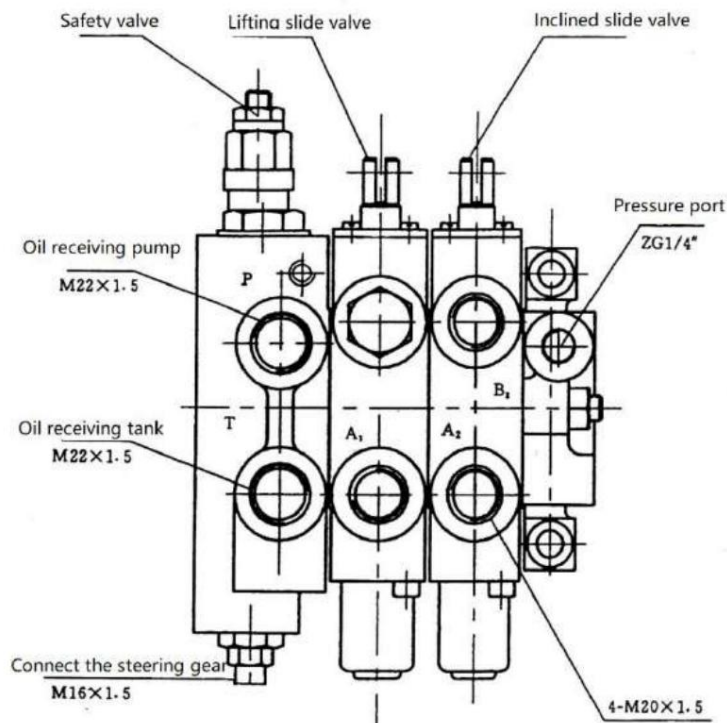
Válvulas multidireccionales para carretillas elevadoras de 1,0 t a 3,8 t
